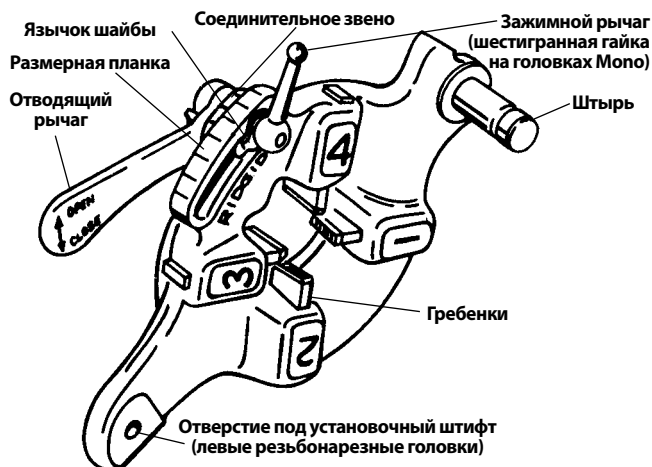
Быстрооткрывающаяся резьбонарезная головка
